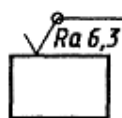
Обозначение одинаковой шероховатости контурной поверхности при знаках
